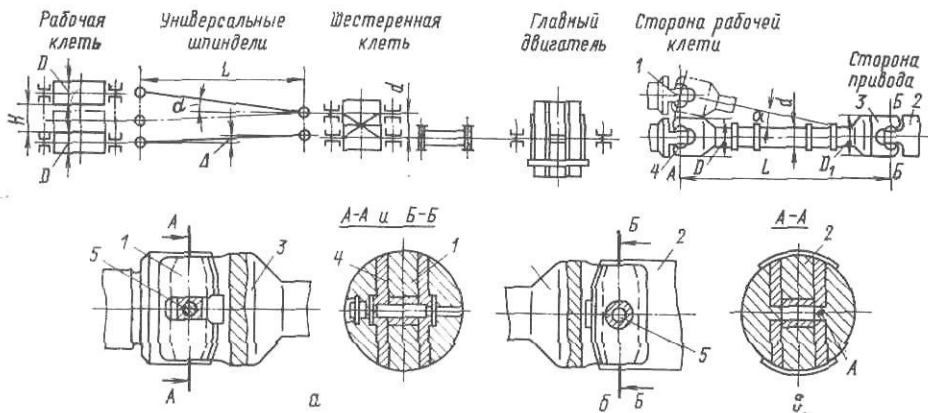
Схема установки универсальных шпинделей и конструктивные элементы шарниров: а — открытый шарнир со стороны валков; б — глухой шарнир со стороны привода; с — сечение шарнира с ребром жесткости посередине расточки
